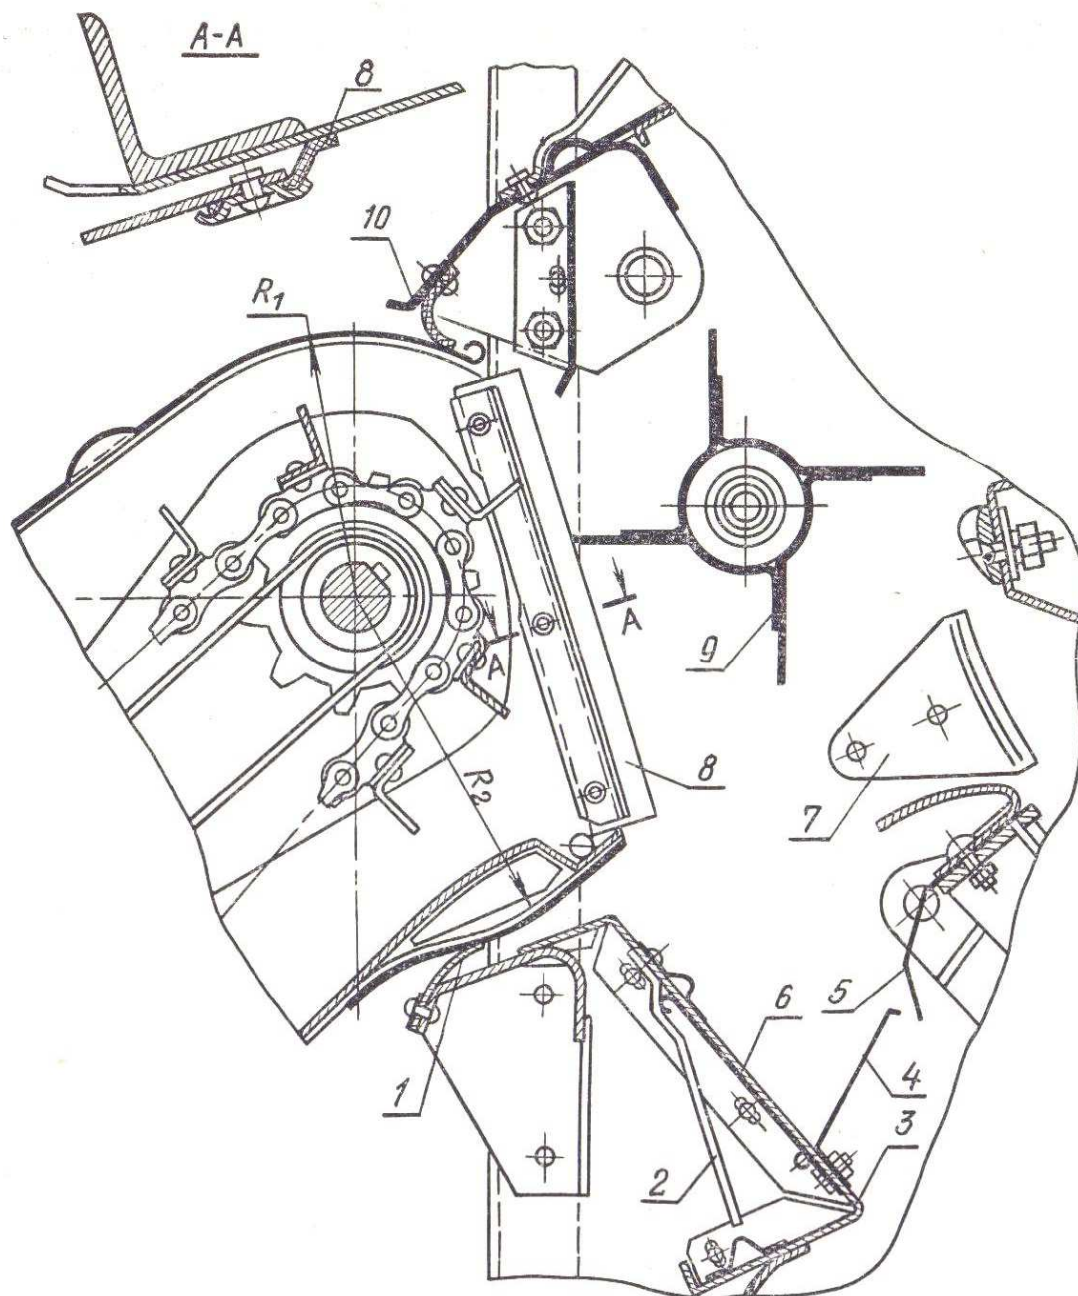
Приемная камера молотилки СК-6: 1 – нижний прорезиненный уплотнитель; 2 – затвор; 3 – передний щиток; 4 – козырек; 5 – козырек передней планки подбарабанья; 6 – крышка люка; 7 – стеблеотвод; 8 – бортовой уплотнитель; 9 – приемный битер; 10 – верхний уплотнитель
